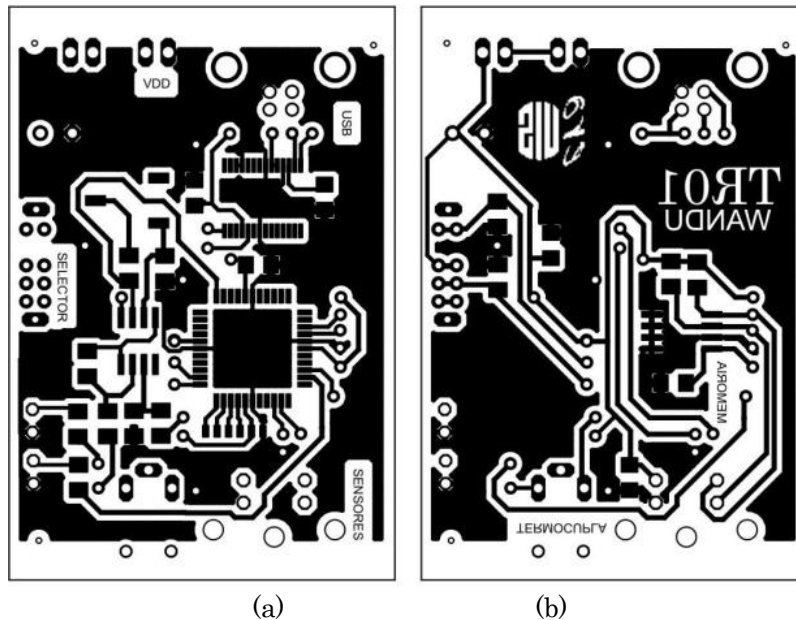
, PCB final del TR01. (a) Top. (b) Bottom.
